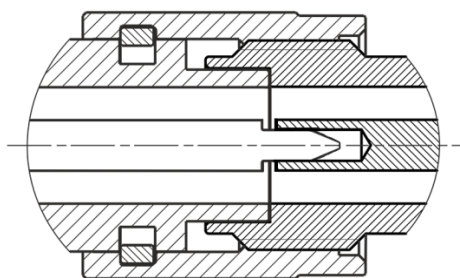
Соединители 3,5 мм и IX (розетка справа, вилка слева)
